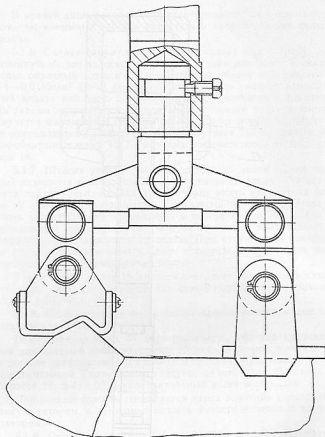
Упор двойной пяточный для обуви 26,5...30,5 размеров.
